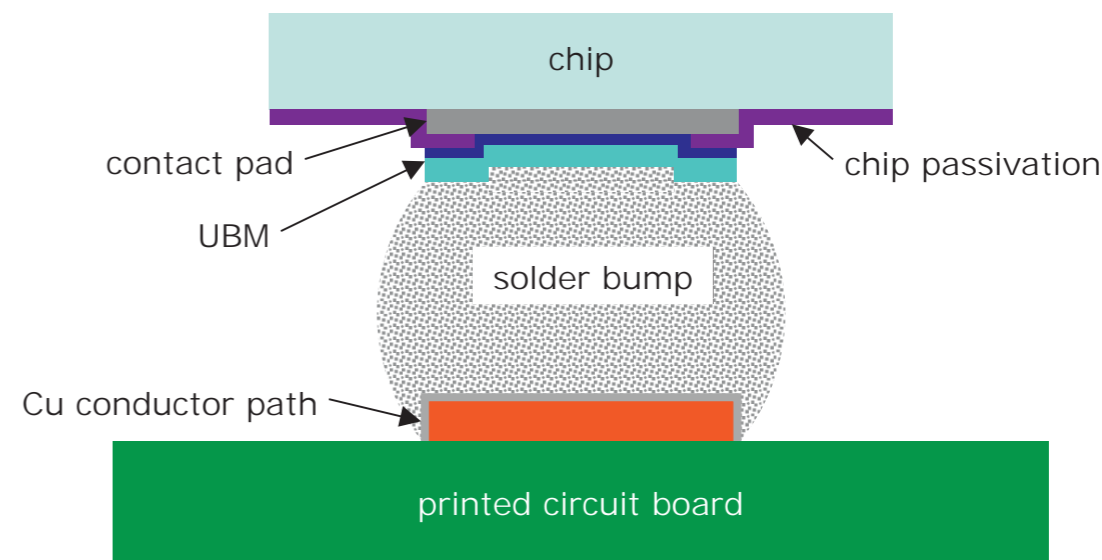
Aufbau der Chip-PCB-Verbindung im Querschnitt.
